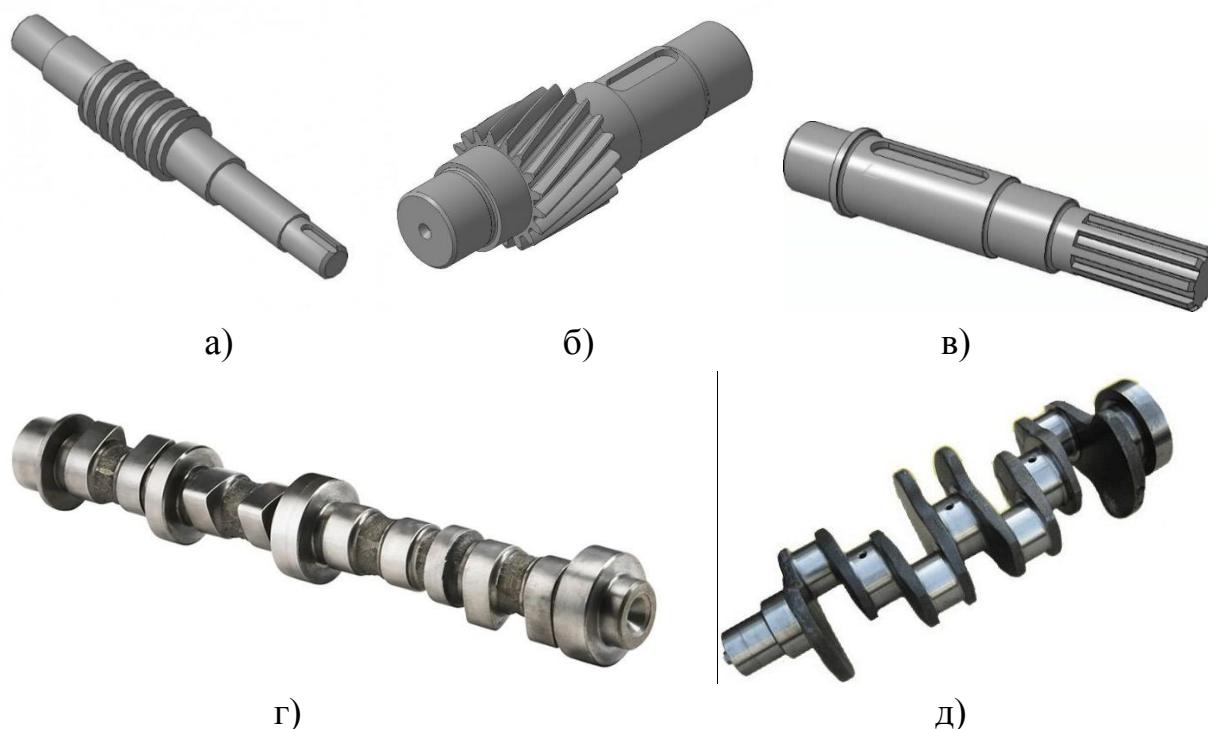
Деякі конструктивні різновиди валів: а – черв'ячний вал, б – вал-шестерня, в – вал шліцевий, г – кулачковий вал, д – колінчастий вал
